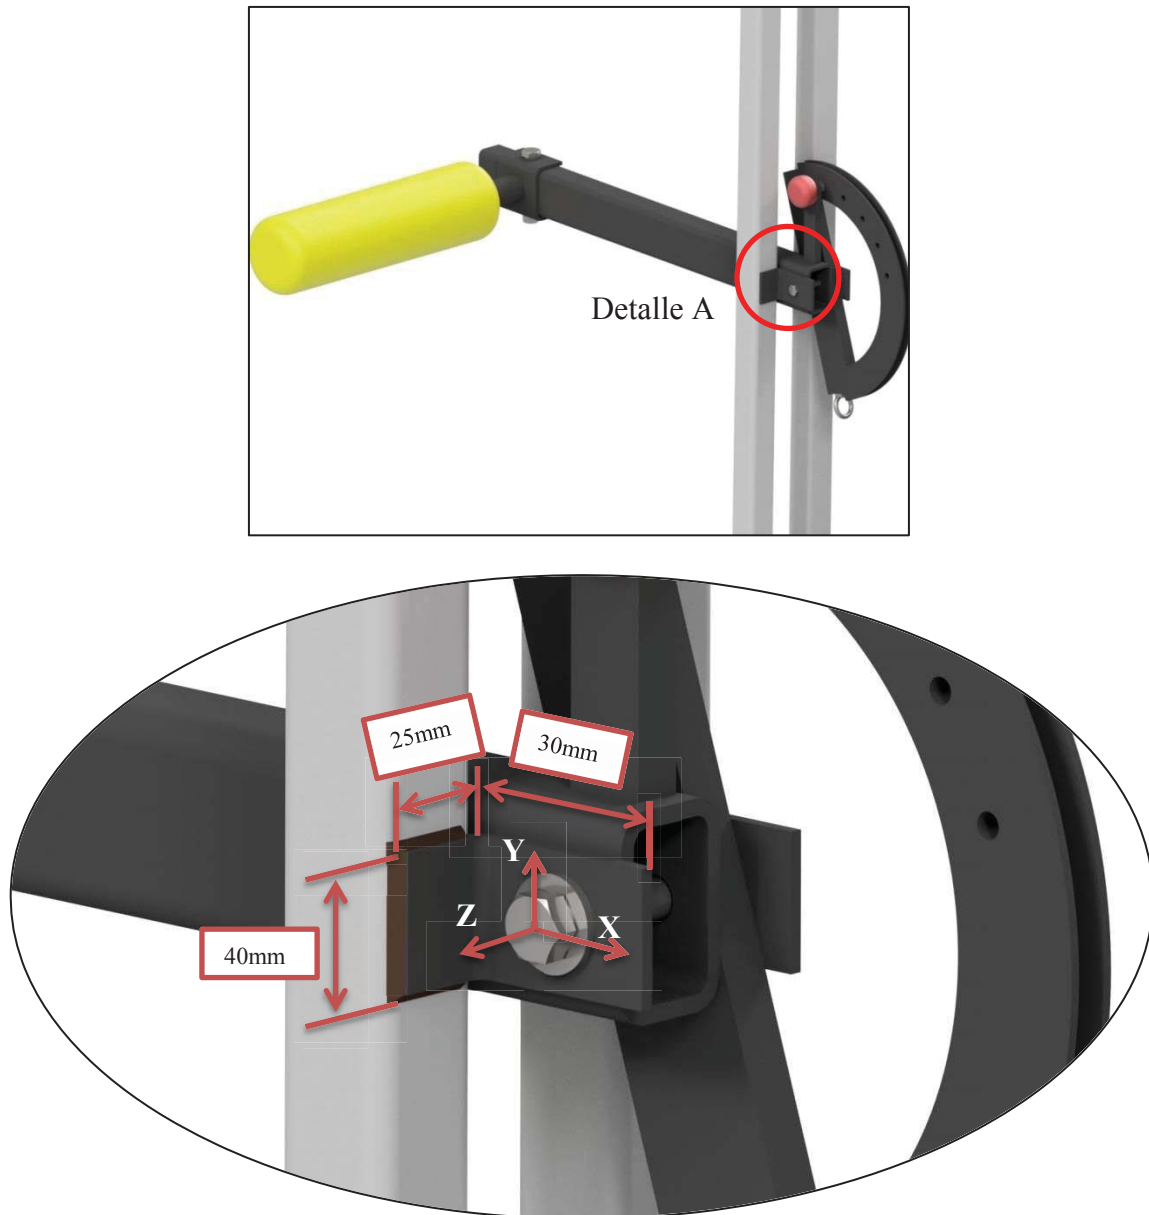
Detalle A, representación de soldadura conjunto 2
